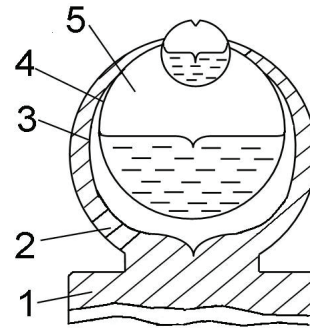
Схема живлення виливка кульового надливу в процесі ЛГМ: 1 — виливок; 2 — надлив; 3 — кірка металу; 4 — коло; 5 — газова фаза
